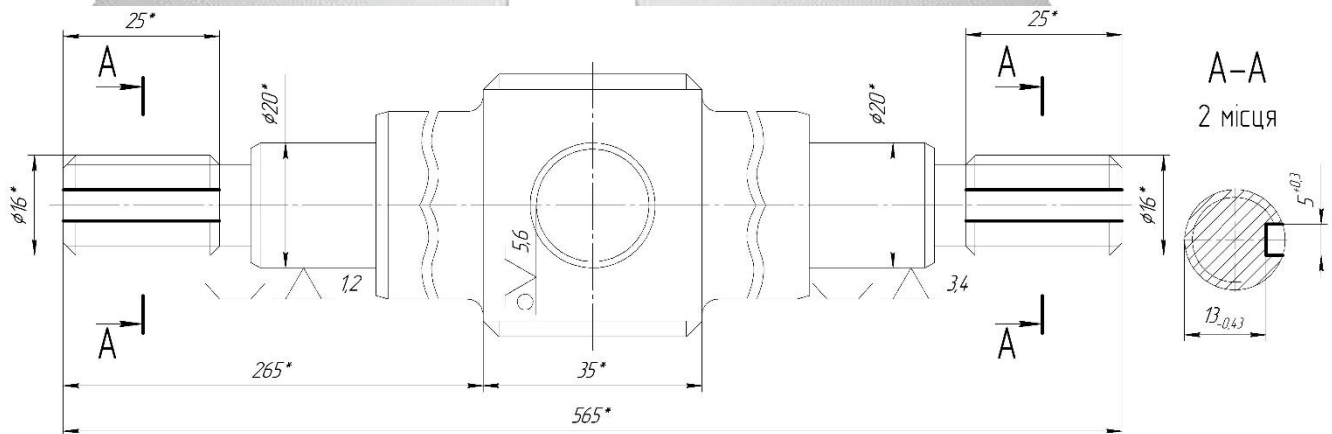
Схема базування заготовки на вертикально-фрезерній з ЧПК операції (перший варіант)
